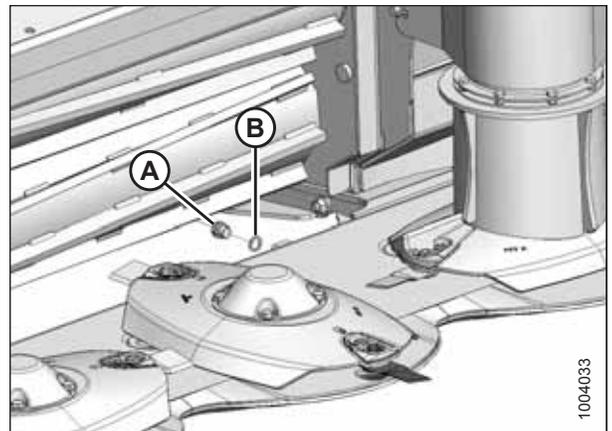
Bouchon d'inspection d'huile de barre de coupe
